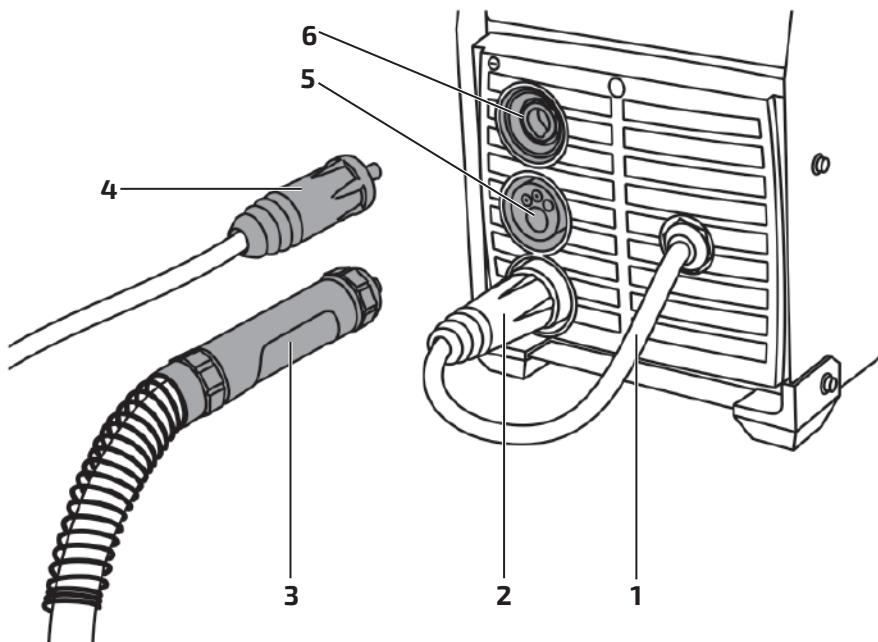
Подключение сварочной горелки MIG/MAG.
